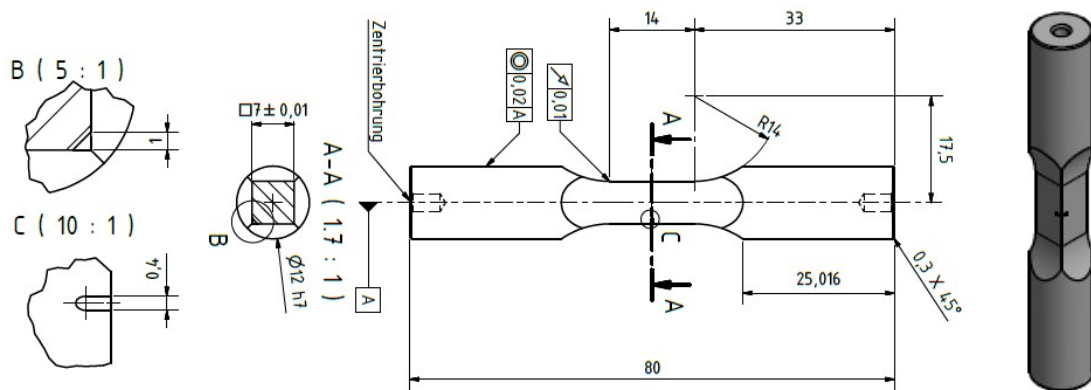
Zeichnung der verwendeten CC-Proben.
